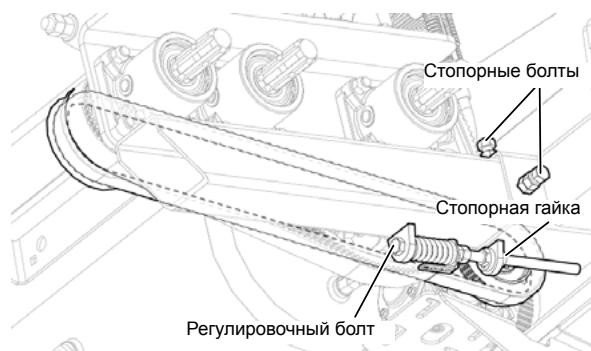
Регулировка натяжения первого приводного ремня левого полотенного транспортера
